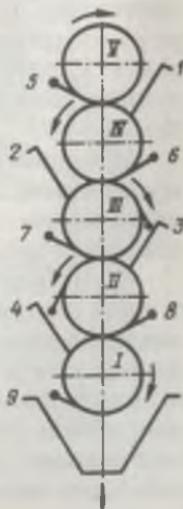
Схема расположения щитов и ножей пятивалкового станка
